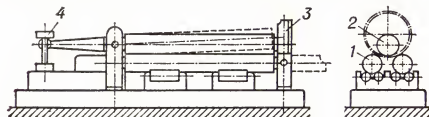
Принципиальная схема трёхвалковой гибочной машины с горизонтальным расположением валков.
